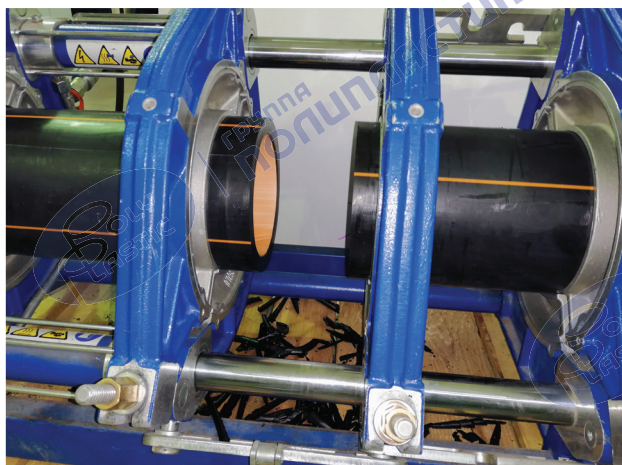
Трубы, установленные в центратор сварочной машины
